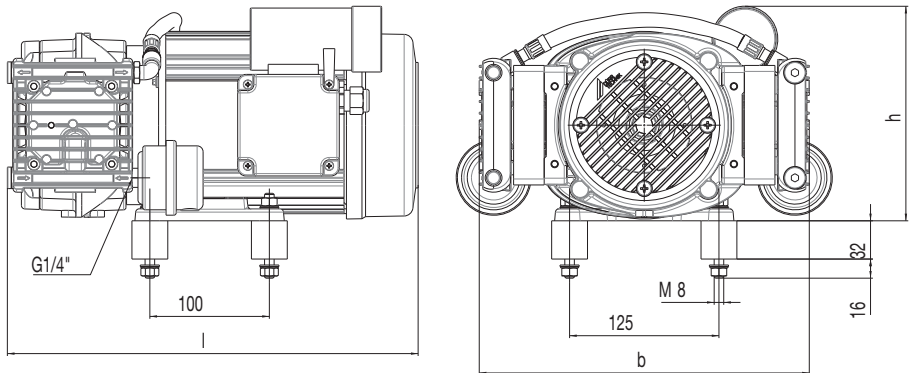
KK40 / KV40; Typ: AG-132; BG-132; AG-065-2E; A-065E; AG-132E; BG-132E
